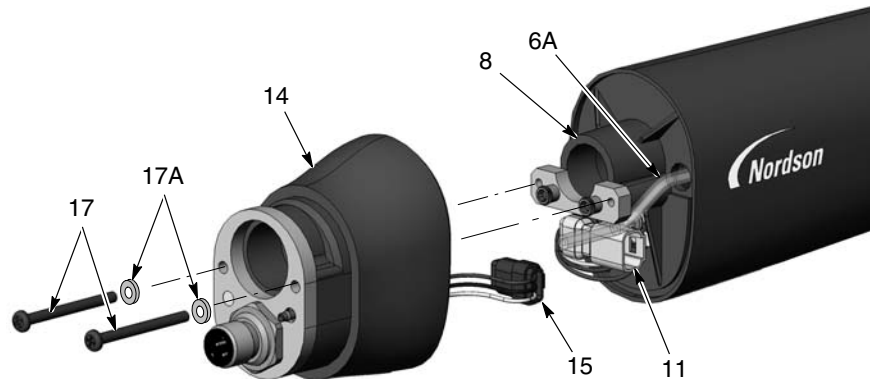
Desmontaje de la pistola de montaje en tubo 3 de 5
